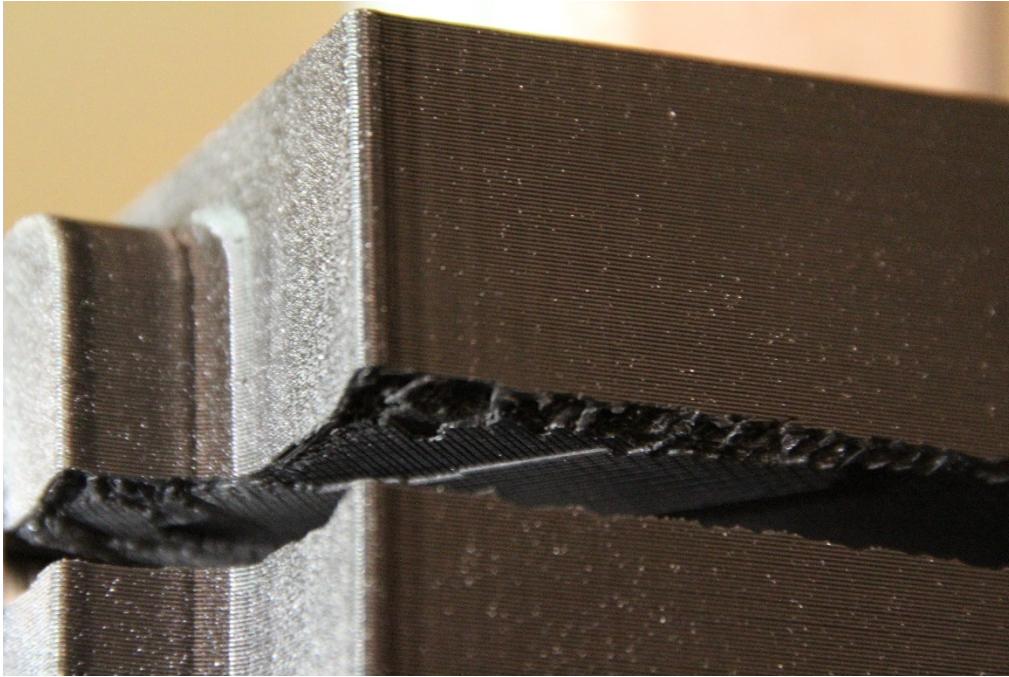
Detalle 3 de rotura del Prototipo 2 a tracción.
